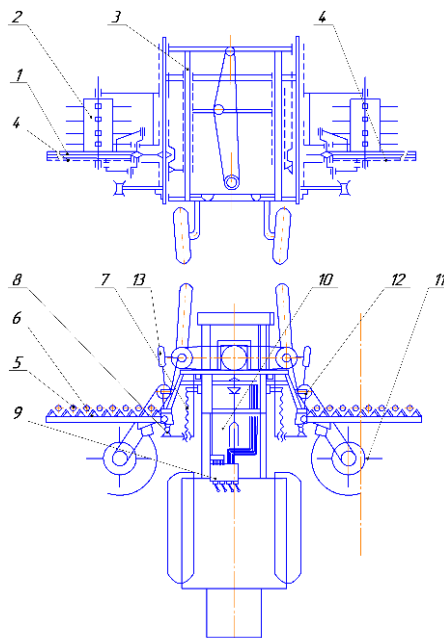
Схема універсальної машини для контурної обрізки виноградників: 1 — косарка, 2 — пристосування для знімання верхівок; 3 — рама косарки; 4 — секції ріжучих апаратів; 5, 11 — захисні пристрої; 6 — проміжна каретка; 7 — пружини; 8, 13 — упори; 9 — гідророзподільник з механізмом управління ріжучими апаратами; 10 — привід; 12 — гідроциліндри
